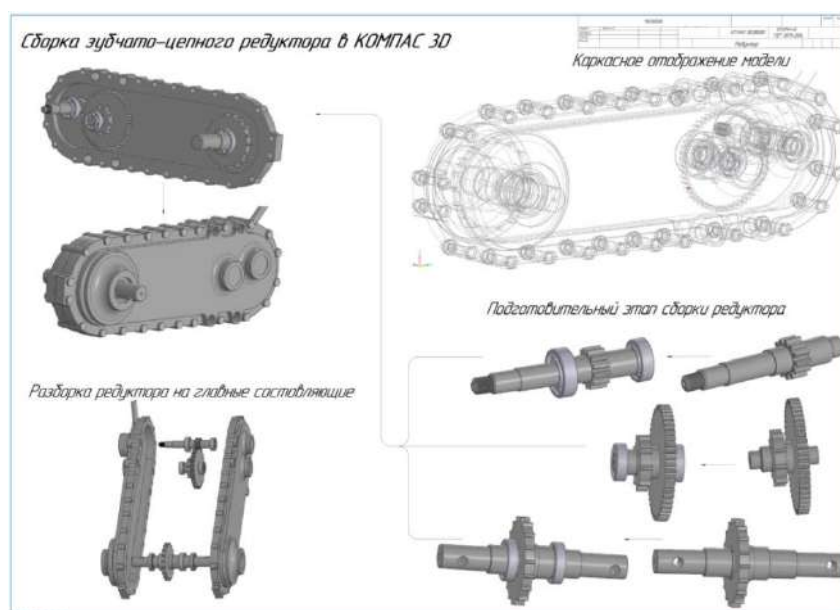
Визуализация сборки зубчато-цепного редуктора.
